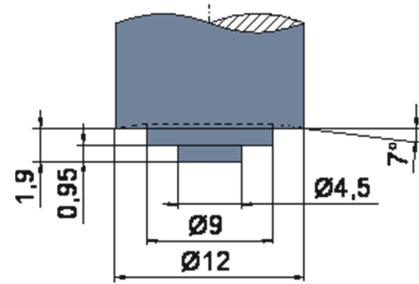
Schmales Werkzeug für Gusslegierung
